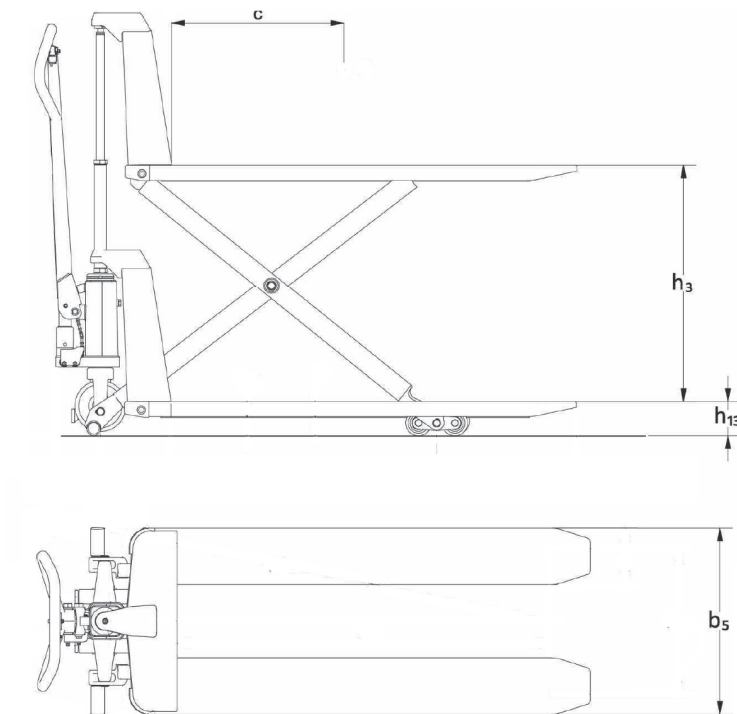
Dimensions du chariot (vue de côté et du dessus, schématiques)
